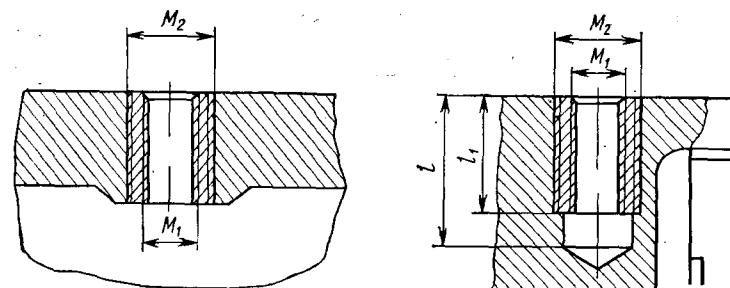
Размеры резьбовых отверстий при ремонте постановкой втулки
